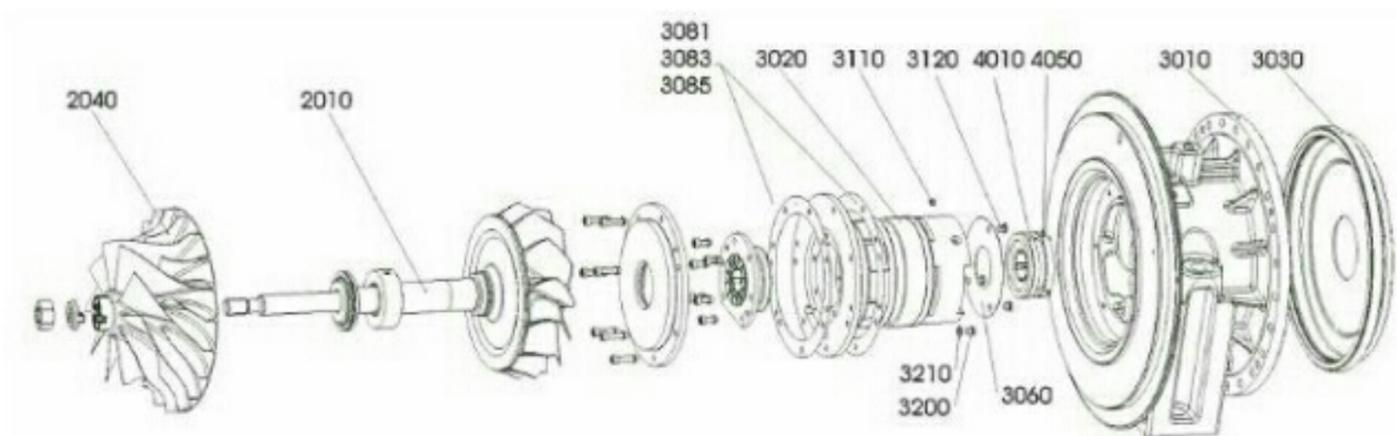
Over haul* pada rotor shaft compressor impeller
